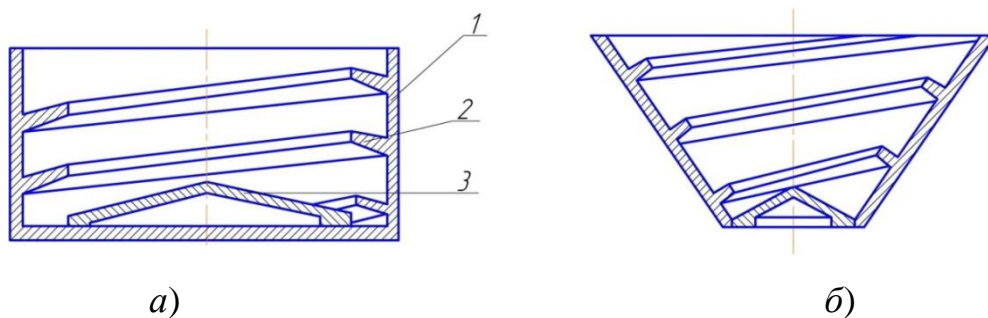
Конструктивні схеми чаш: *а)* – циліндрична; *б)* – конічна
